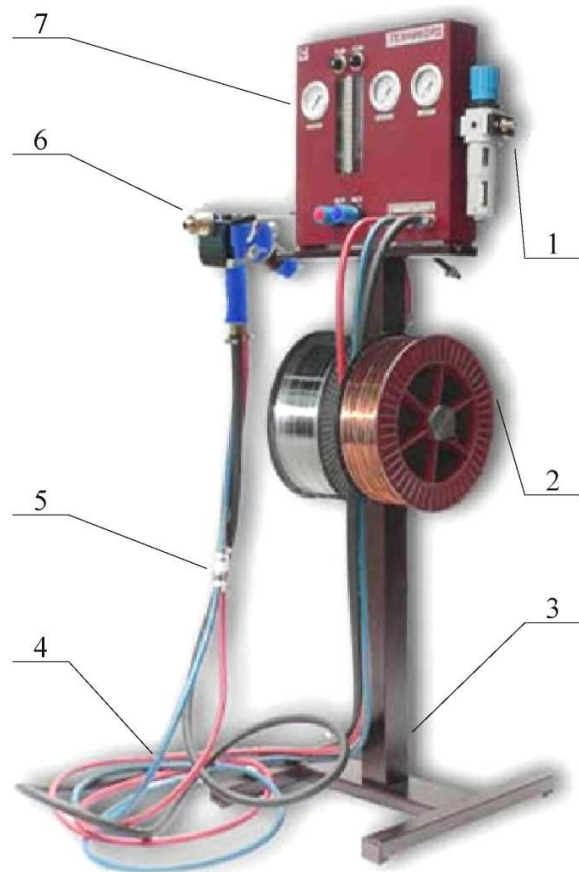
Фотография универсальной установки для нанесения покрытий: 1 – блок подготовки воздуха; 2 – катушки с проволокой или гибким шнуром; 3 – стойка; 4 – резиноканевые шланги; 5 – защитные клапаны; 6 – пистолет-распылитель «ТЕНА ТОП-ЖЕТ/2»; 7 – пульт управления рабочими газами ПУ-03
